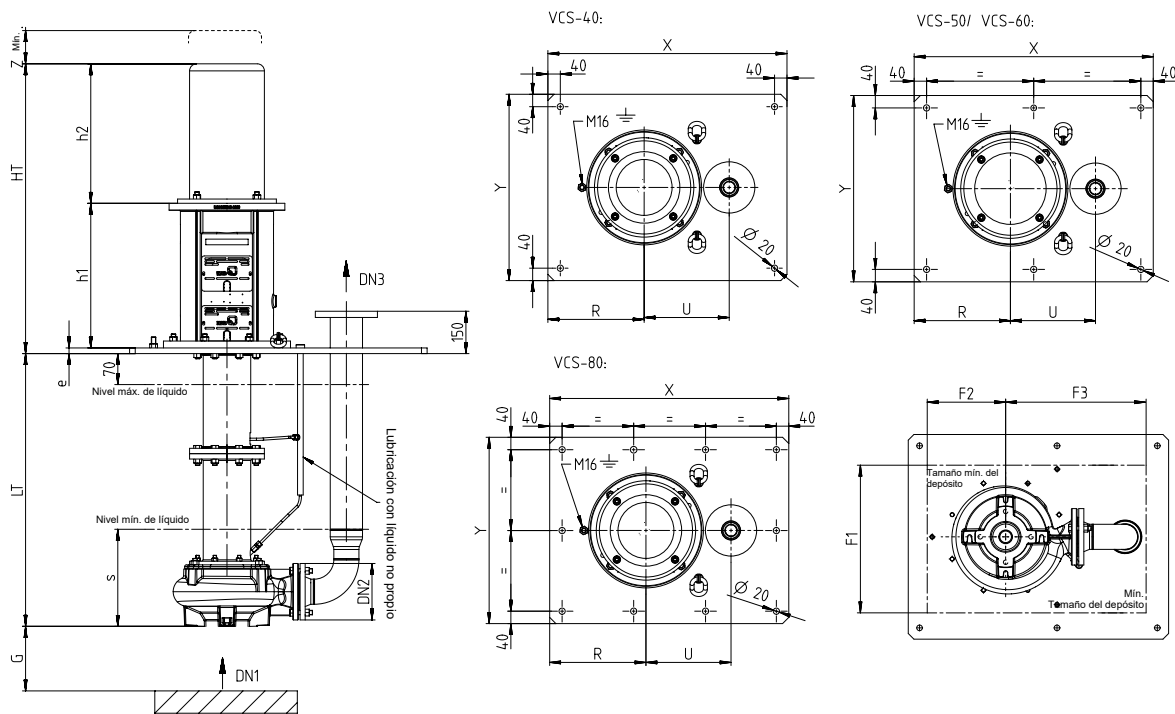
Dimensiones de la bomba y profundidades de inmersión, bancada rectangular
